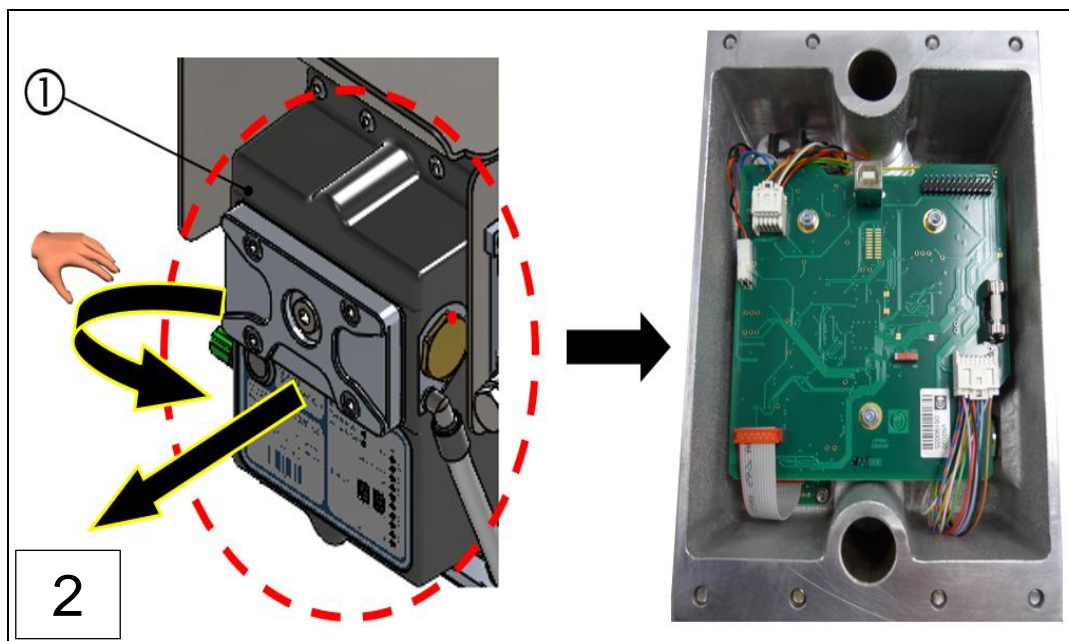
Smontaggio dispositivo di misurazione VN200 (passaggi del montaggio 1 - 2)
